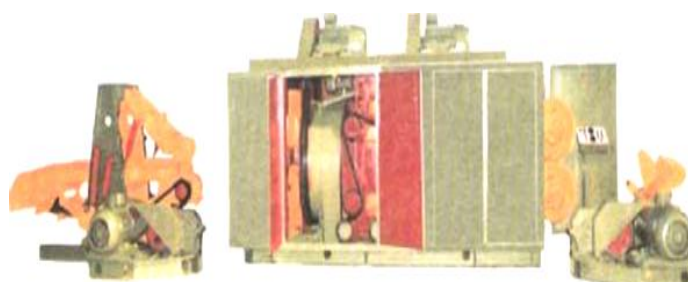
Опытный образец головного станка гаммы нового поколения с гидроприводом механизма подачи ОК63-3
